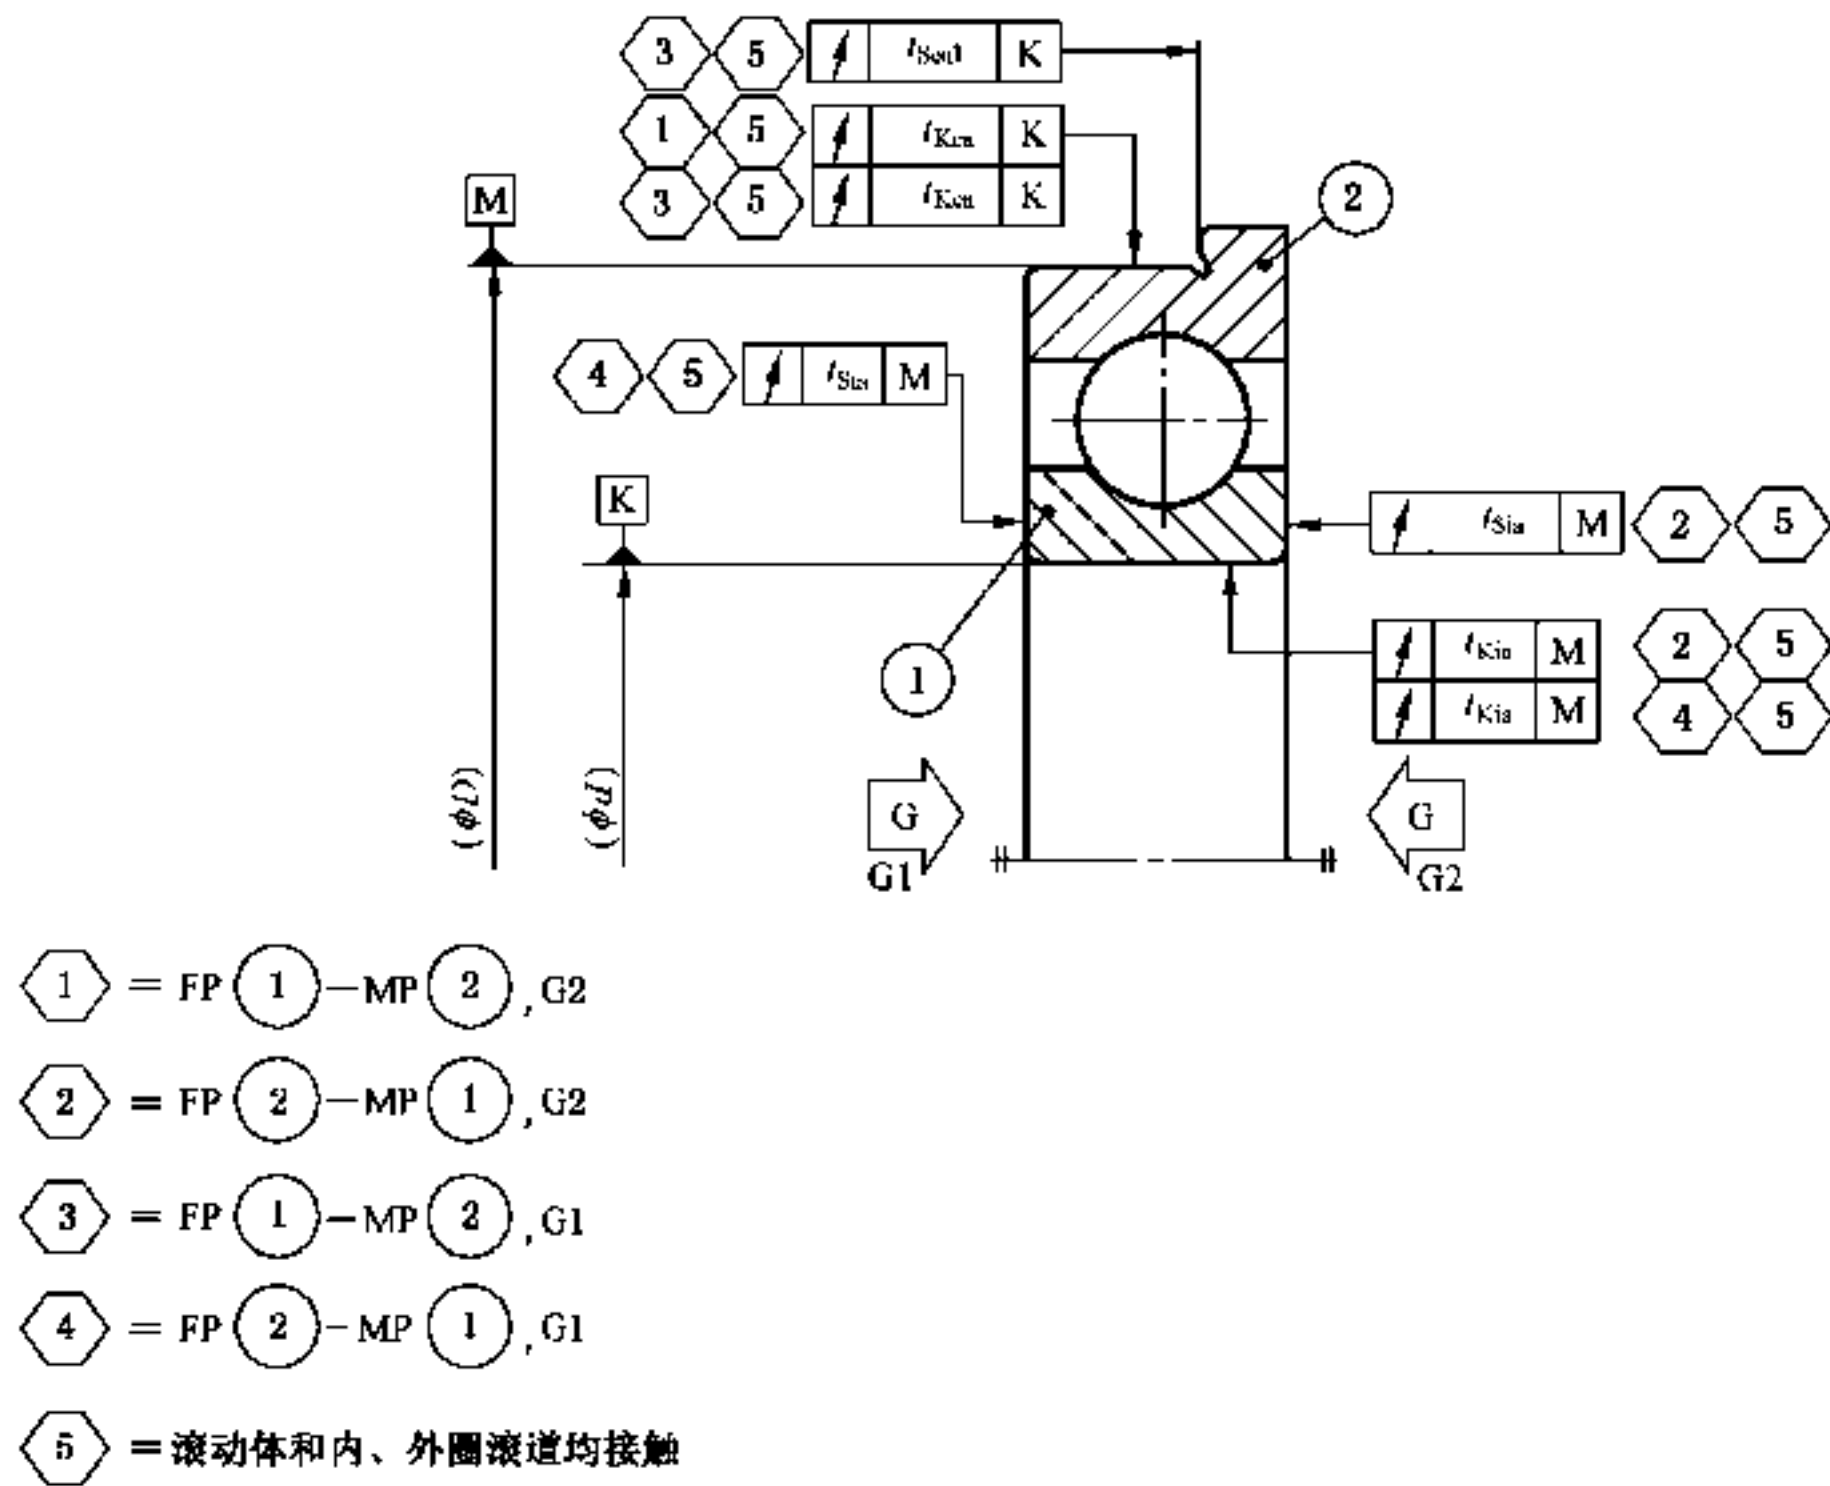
凸缘外圈成套轴承的几何公差——深沟球轴承、双列深沟球轴承、双列角接触球轴承和四点接触球轴承
